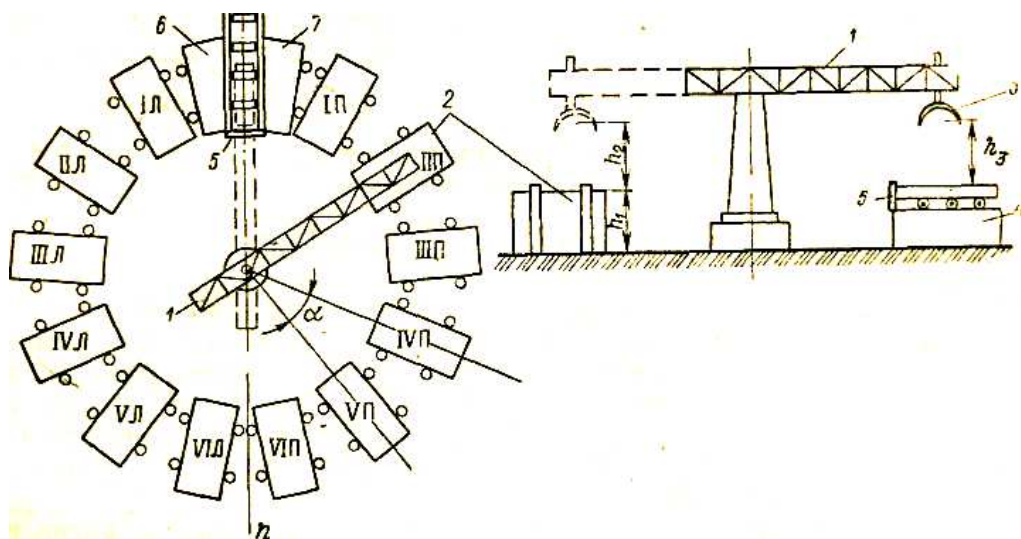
Схема сортировочно-пакетирующего участка с манипулятором
